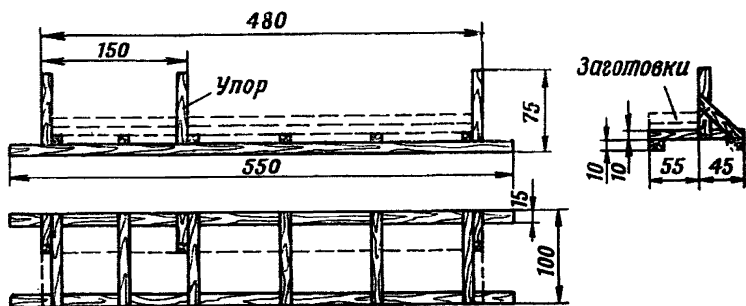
Кондуктор для опиловки досок щитов проезжей части
